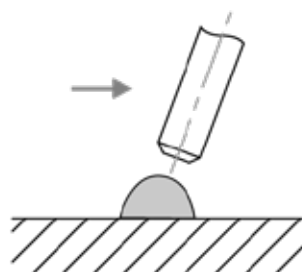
Влияние длины дуги и скорости сварки.
